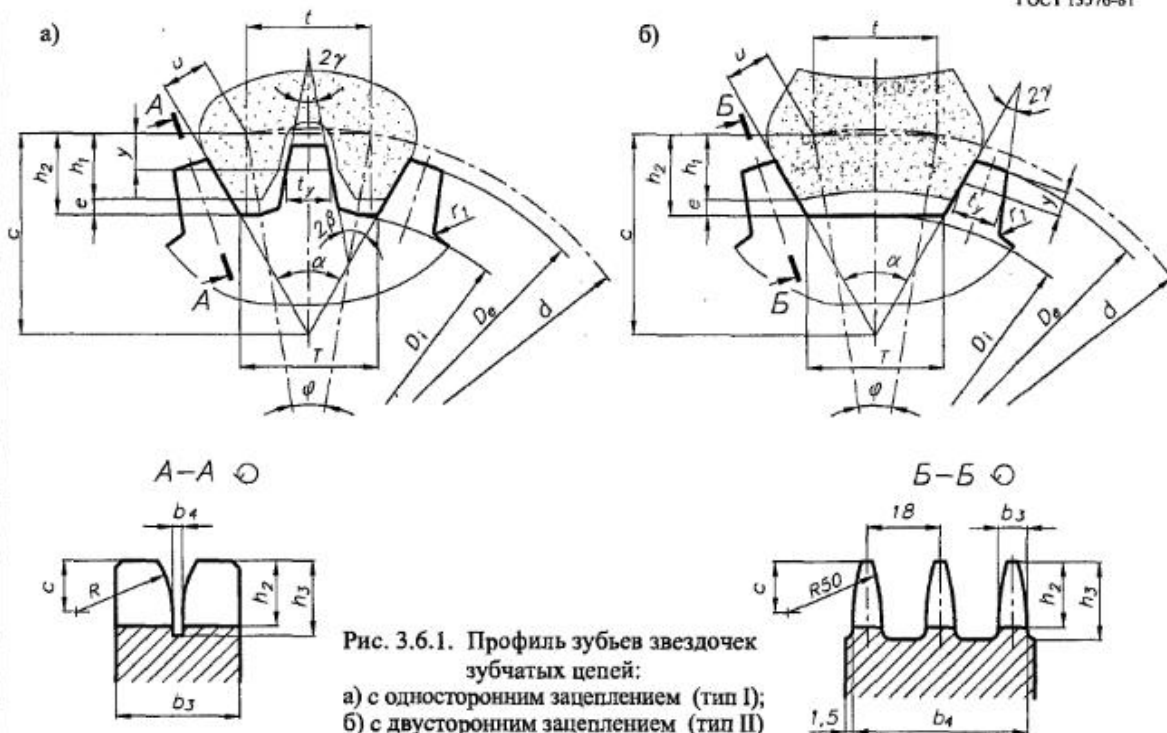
Профиль зубьев звездочек зубчатых цепей:
